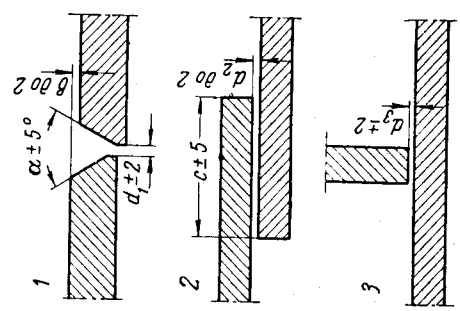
Допуски на сборку для сварки.
